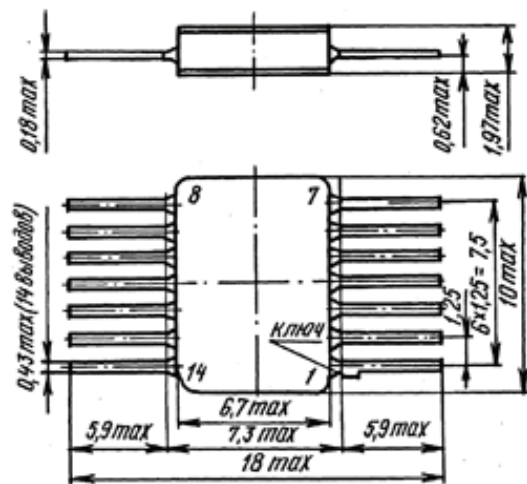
Габаритные чертежи корпусов 401.14-4 и 401.14-5М
